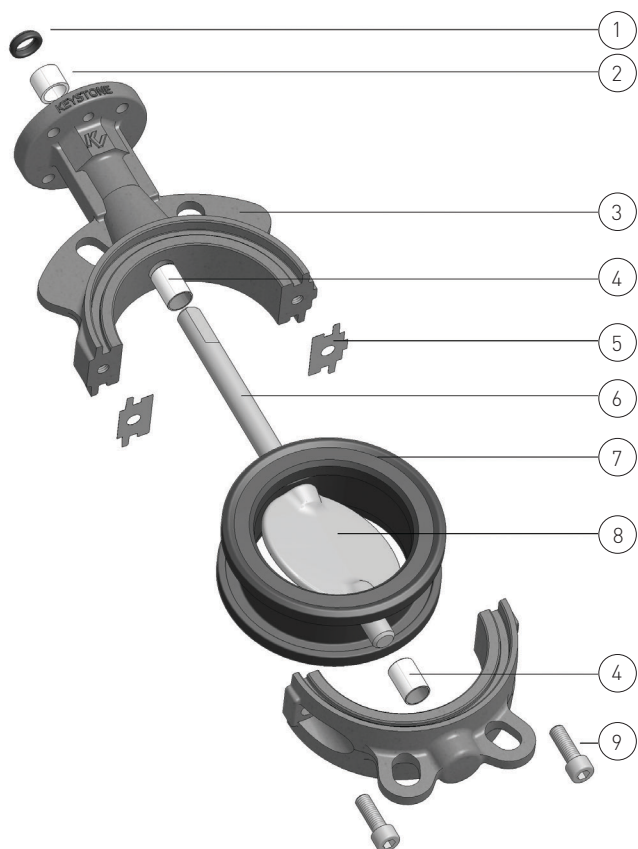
/16 разнесенный вид (корпуса из ковкого чугуна)
